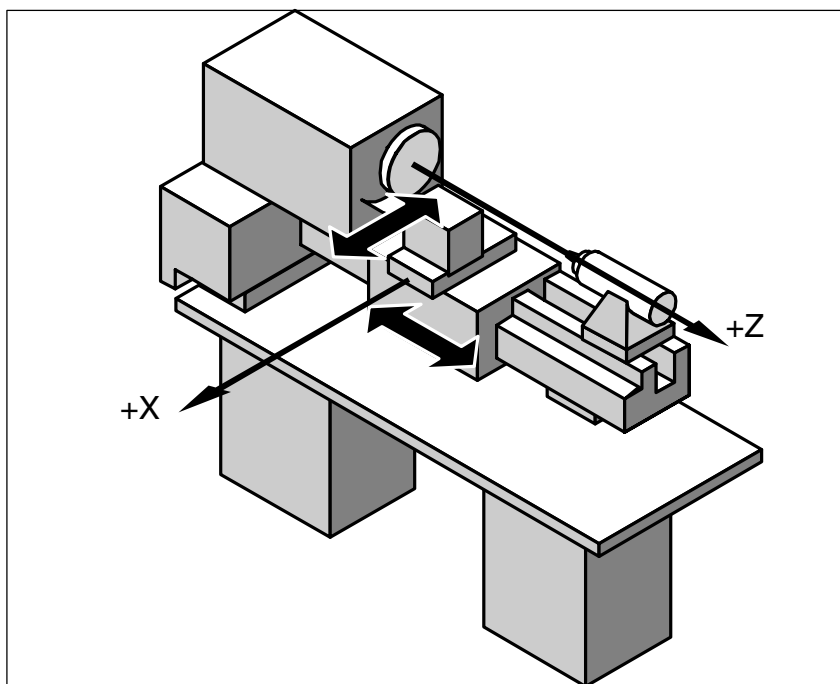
Coordenadas/ejes de máquina en el ejemplo del torno
